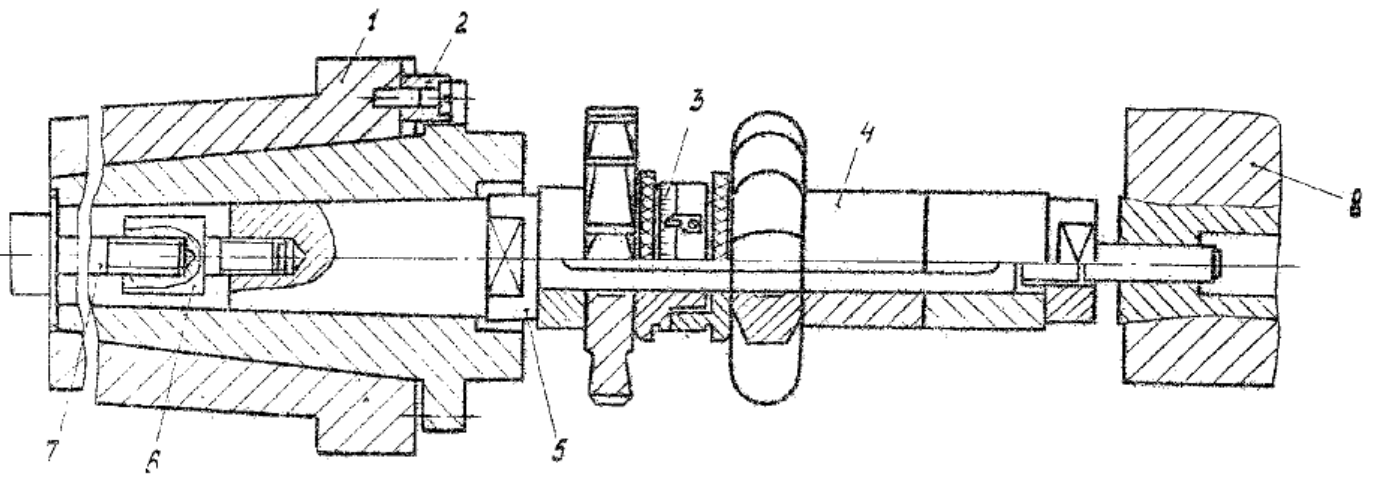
Установка фрезы на оправке горизонтально – фрезерного станка:
